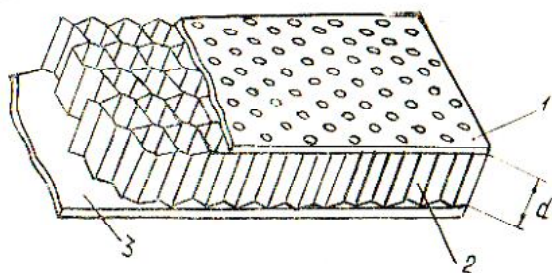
Схема однослойной сотовой звукопоглощающей конструкции: 1-перфорированный лист; 2-сотовая конструкция; 3-непроницаемый лист
